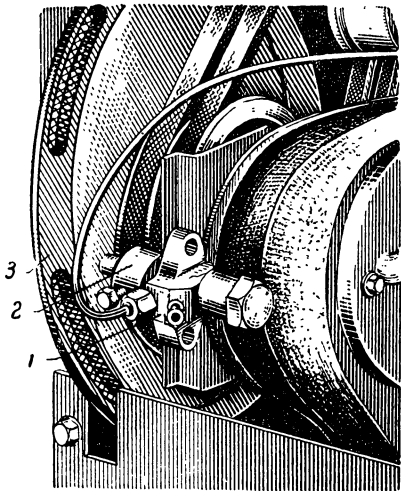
Приспособление для определения величины угла опережения подачи топлива:
